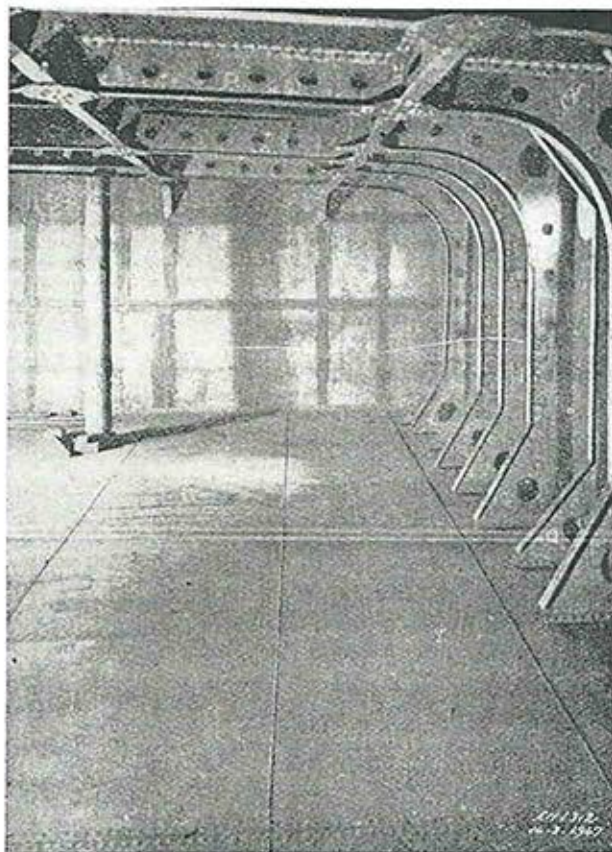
Vista de una cubierta soldada en los destructores.
